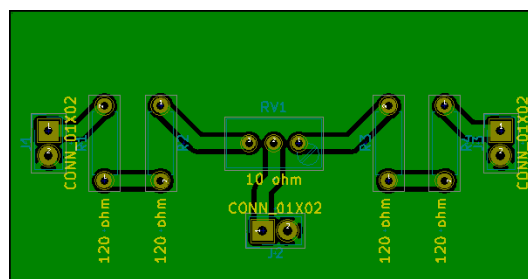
PCB Conexión Bobinas de Sensado – Banco de Pruebas N° 2
